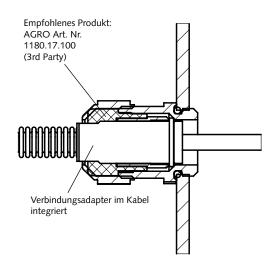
Kabel mit hermetisch dichtem Wellschlauch
